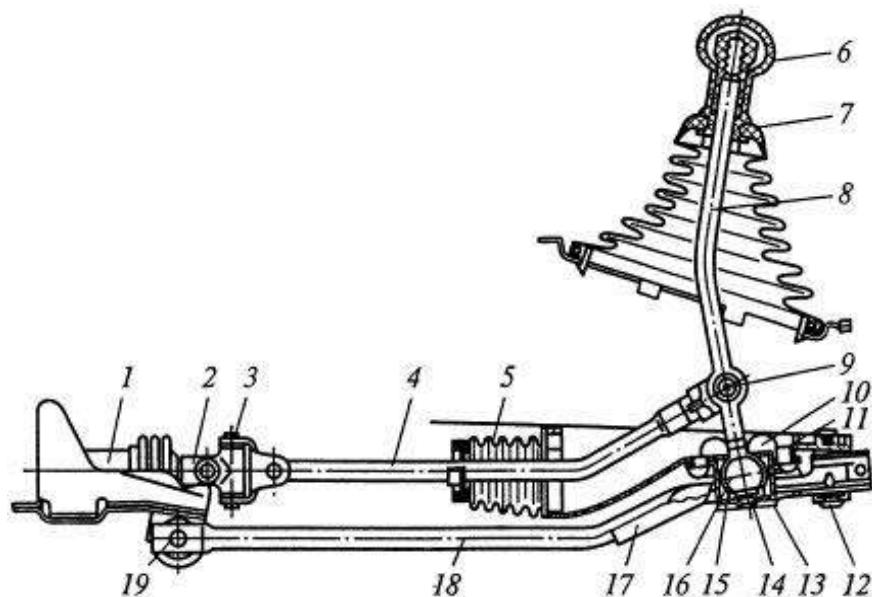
Механизм переключения передач двухвальной коробки передач автомобиля АЗЛК:
